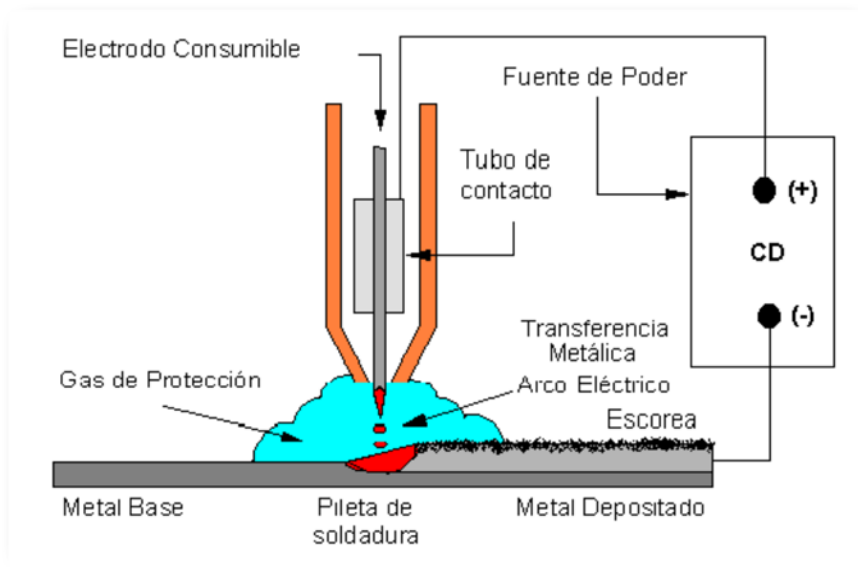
Proceso de Soldadura GMAW.
